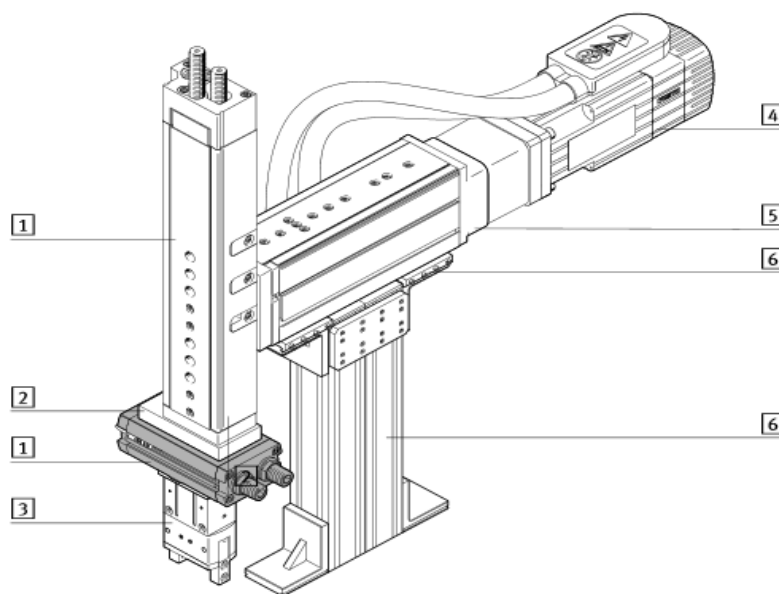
Kombinovaný lineární a kyvný motor [1]
